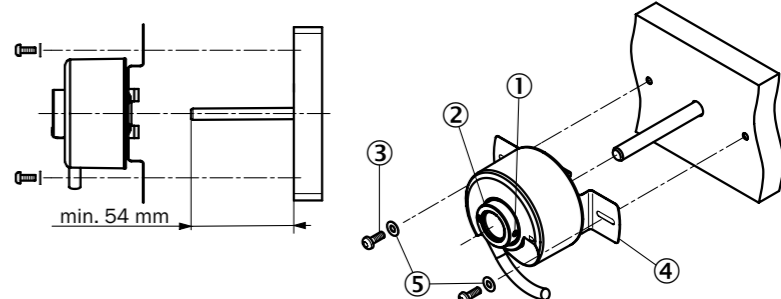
Anbau DBS60 Core Klemmflansch über flanschseitige Gewindebohrungen
